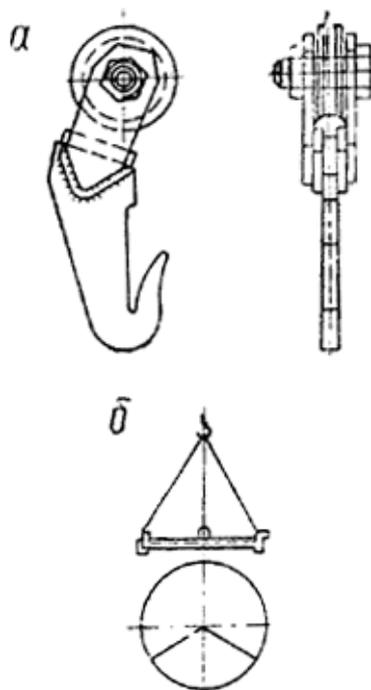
Тросовый захват для транспортировки днищ и резервуаров: а — крюк захвата; б — схема строповки днища захватом
